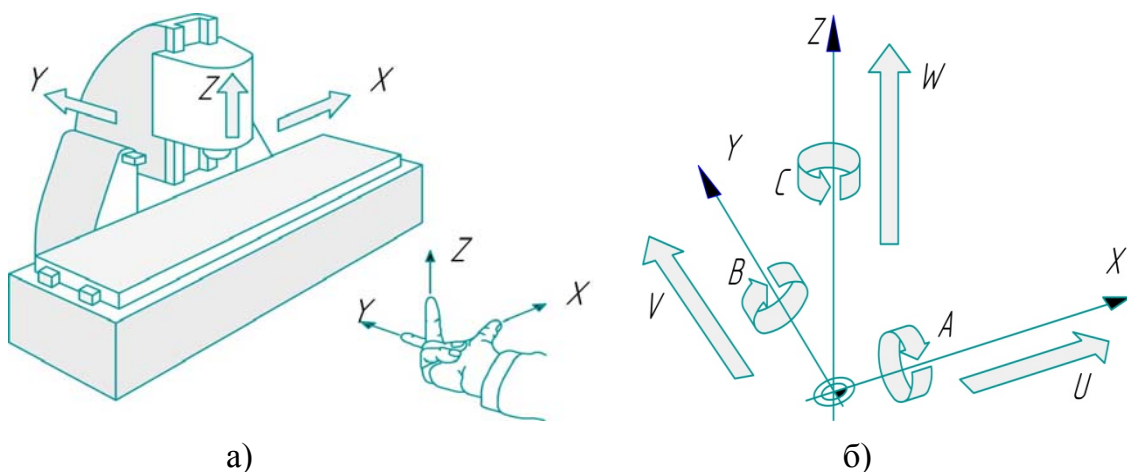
Система координат фрезерного станка с ЧПУ (а) и виды осей (б)
